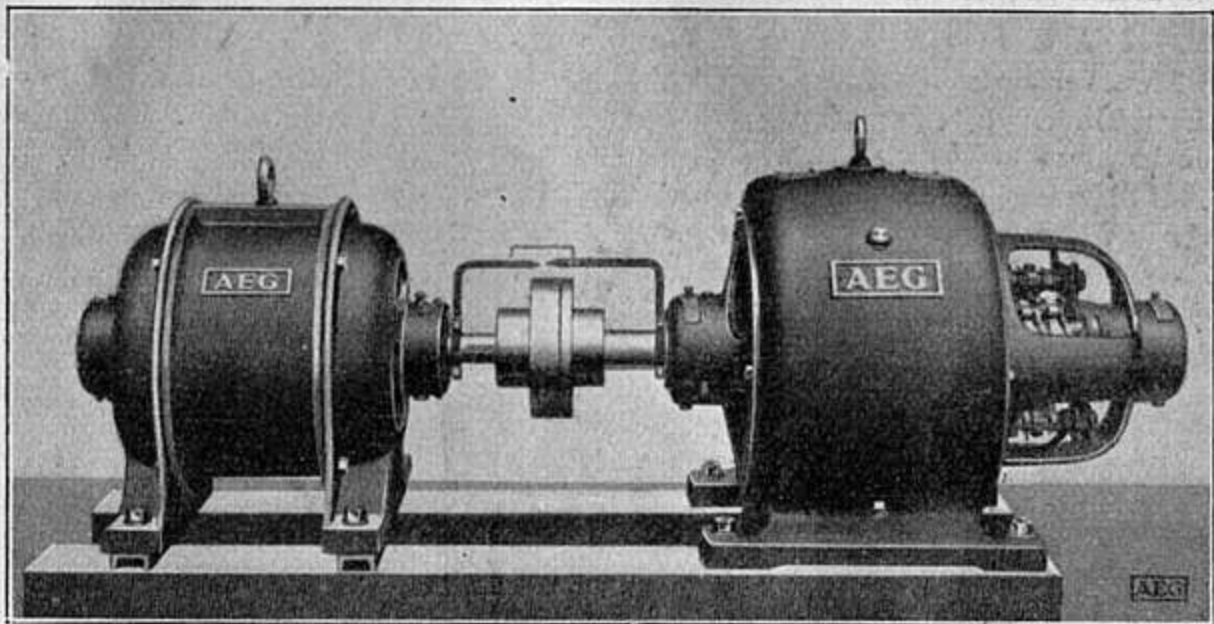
Ausrichten zu kuppelnder Maschinen.
